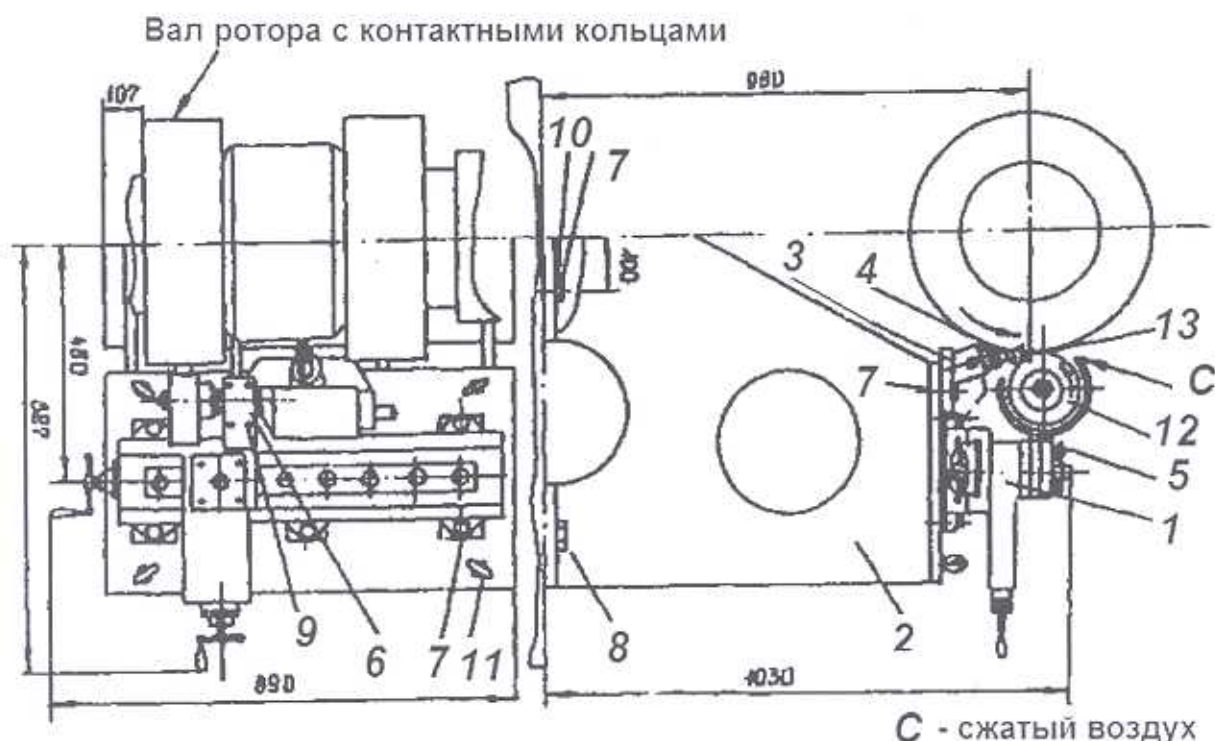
Приспособление для проточки и шлифовки контактных колец турбогенераторов ТГВ-300:
